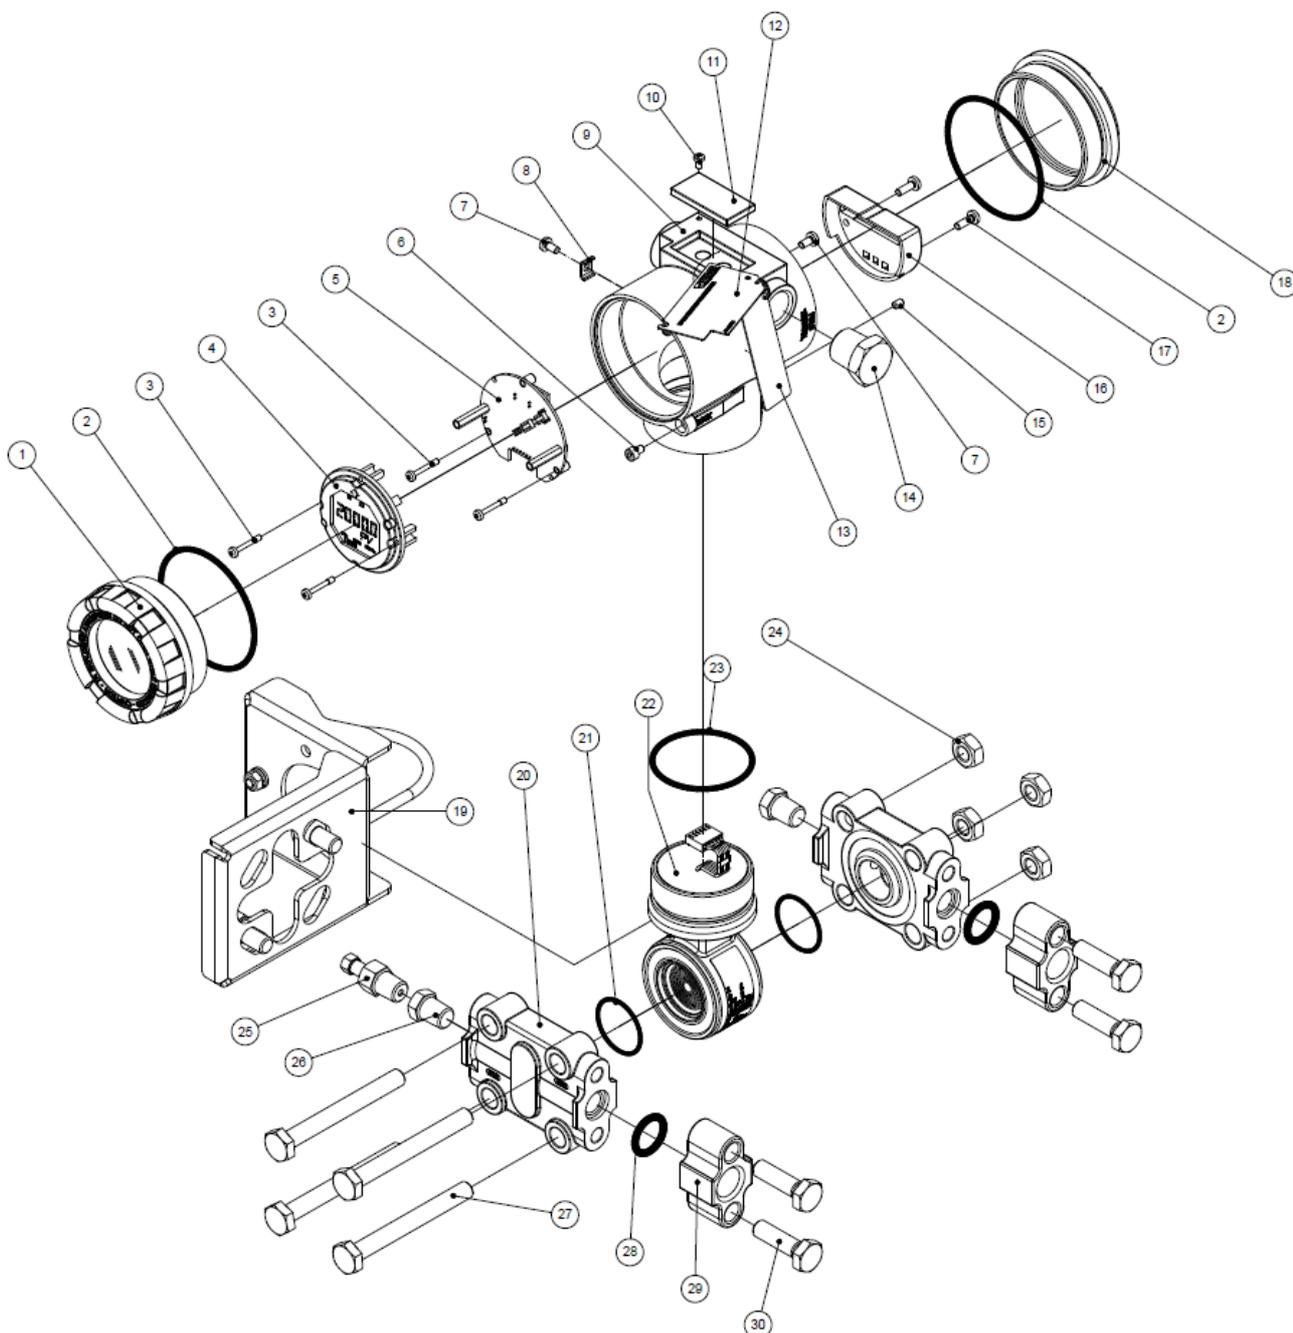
Desenho explodido do sensor de pressão alta (HIGH) do VDL10 HART.
